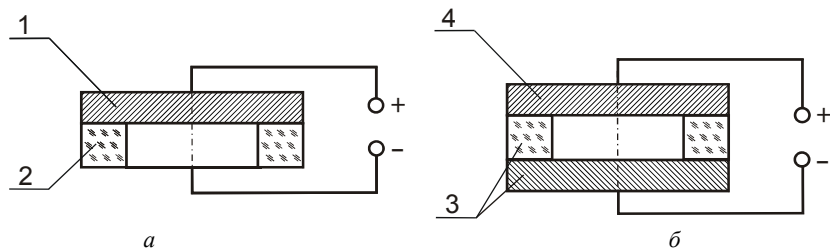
Принципова схема зварювання багатошарових структур [3]:
